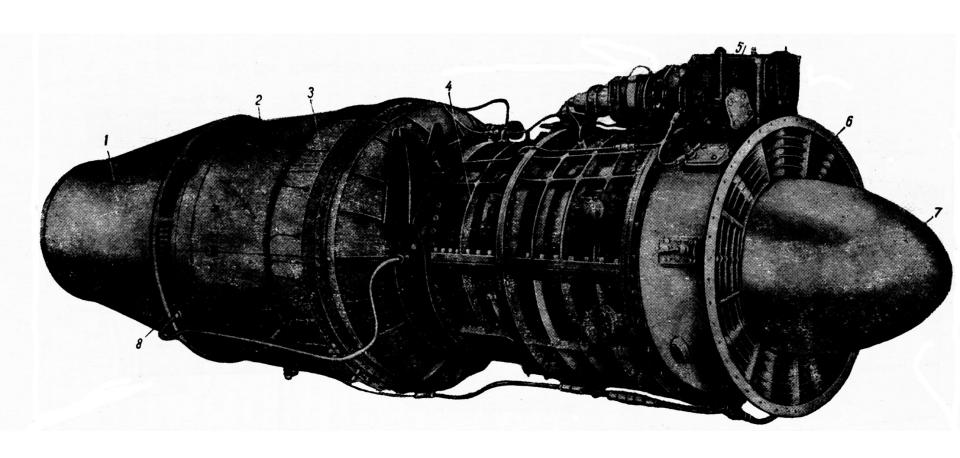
Общий вид двухконтурного турбореактивного двигателя
